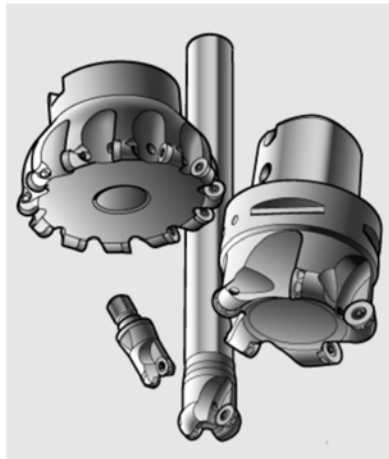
Фрезы с круглыми пластинами для черновых операций
